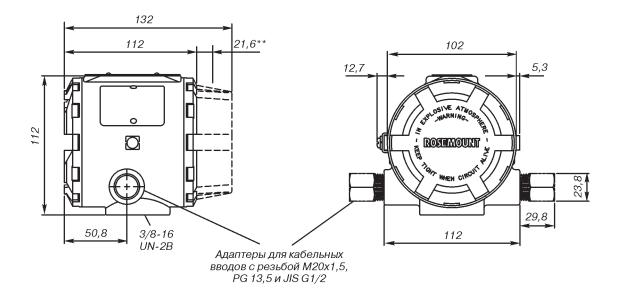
Габаритный чертеж преобразователя. Кабельный ввод M20x1,5; PG13,5 и JIS G1/2\*.
